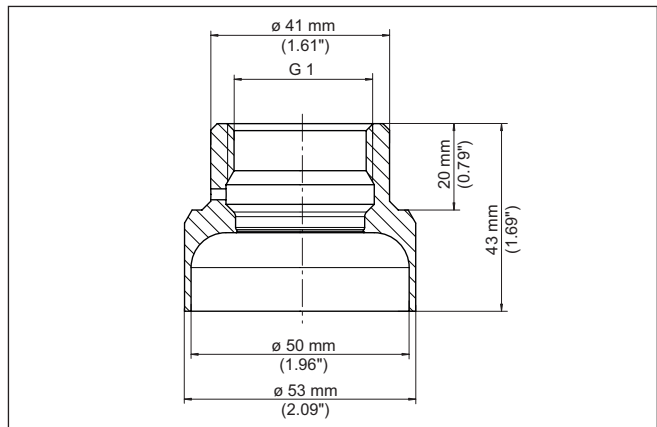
Maße Direkt-Einschweißstutzen für Rohrmontage G1 (ISO 228-1) - O-Ring-Dichtung
